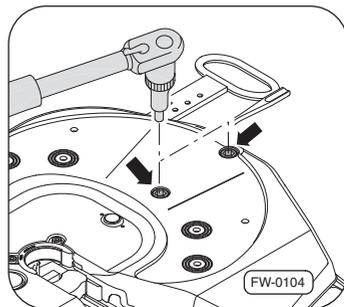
· Демонтаж пластины седельно-сцепного устройства с крепления опорного подшипника
